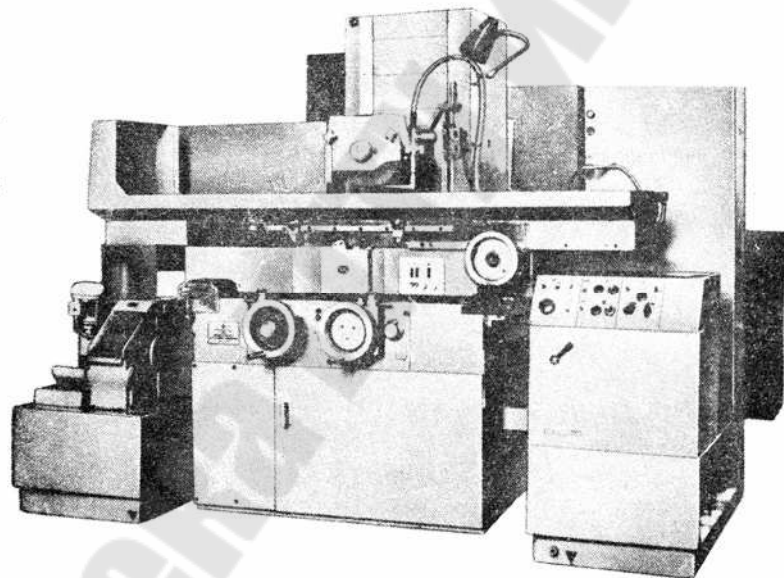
Внешний вид плоскошлифовального станка модели 3E711B
